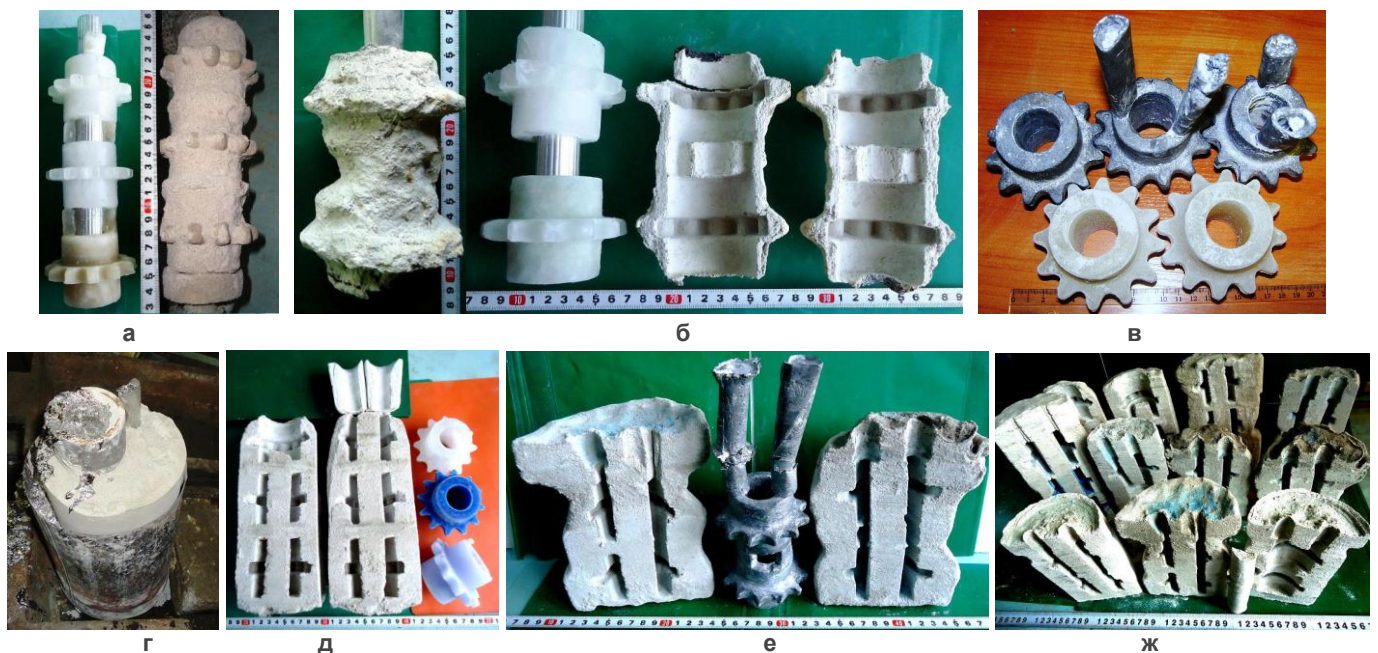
Примеры ЛМ, оболочковых форм и отливок: а - блок из трех моделей и 3-местная форма; б - блок из двух моделей и распиленная 2-местная форма; в - примеры отливок и ЛМ; г - залитая форма; д - распиленная 3-местная форма и отдельные модели разной окраски; е - распиленная 2-местная форма и отливка по такой форме; ж - распиленные 2- и 3-местные формы.
